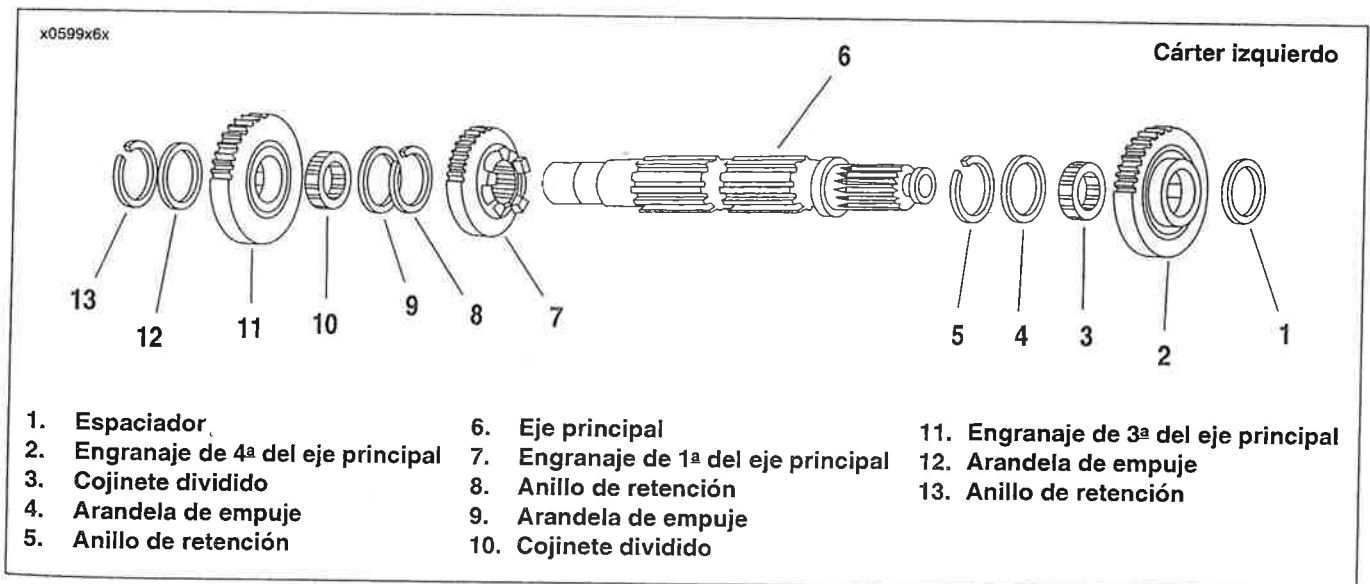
Rearmado del conjunto del eje principal de la transmisión
